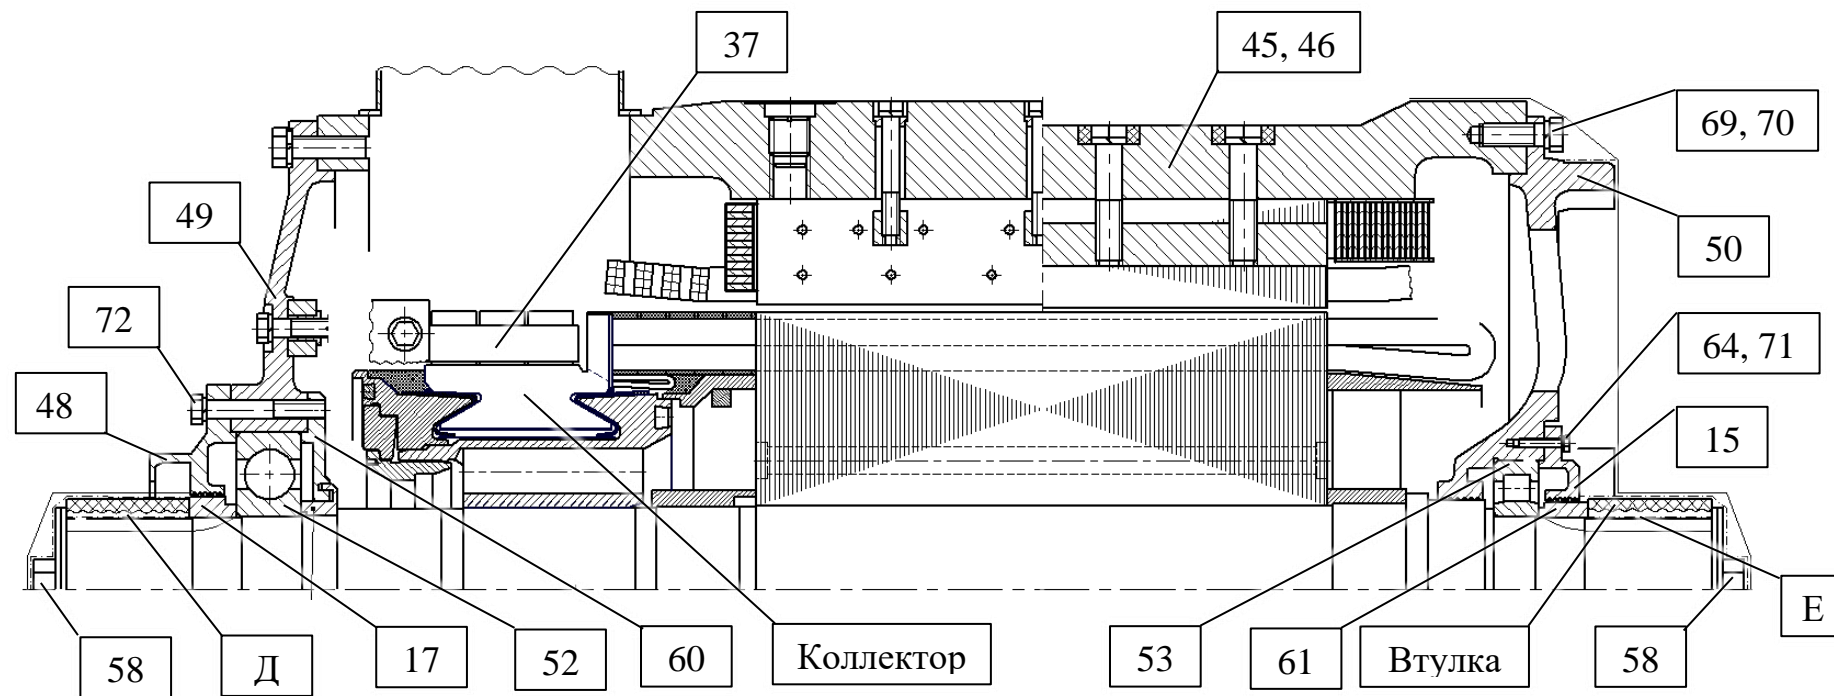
Общий вид электродвигателя тягового ЭДП-600; ЭДП-600С
